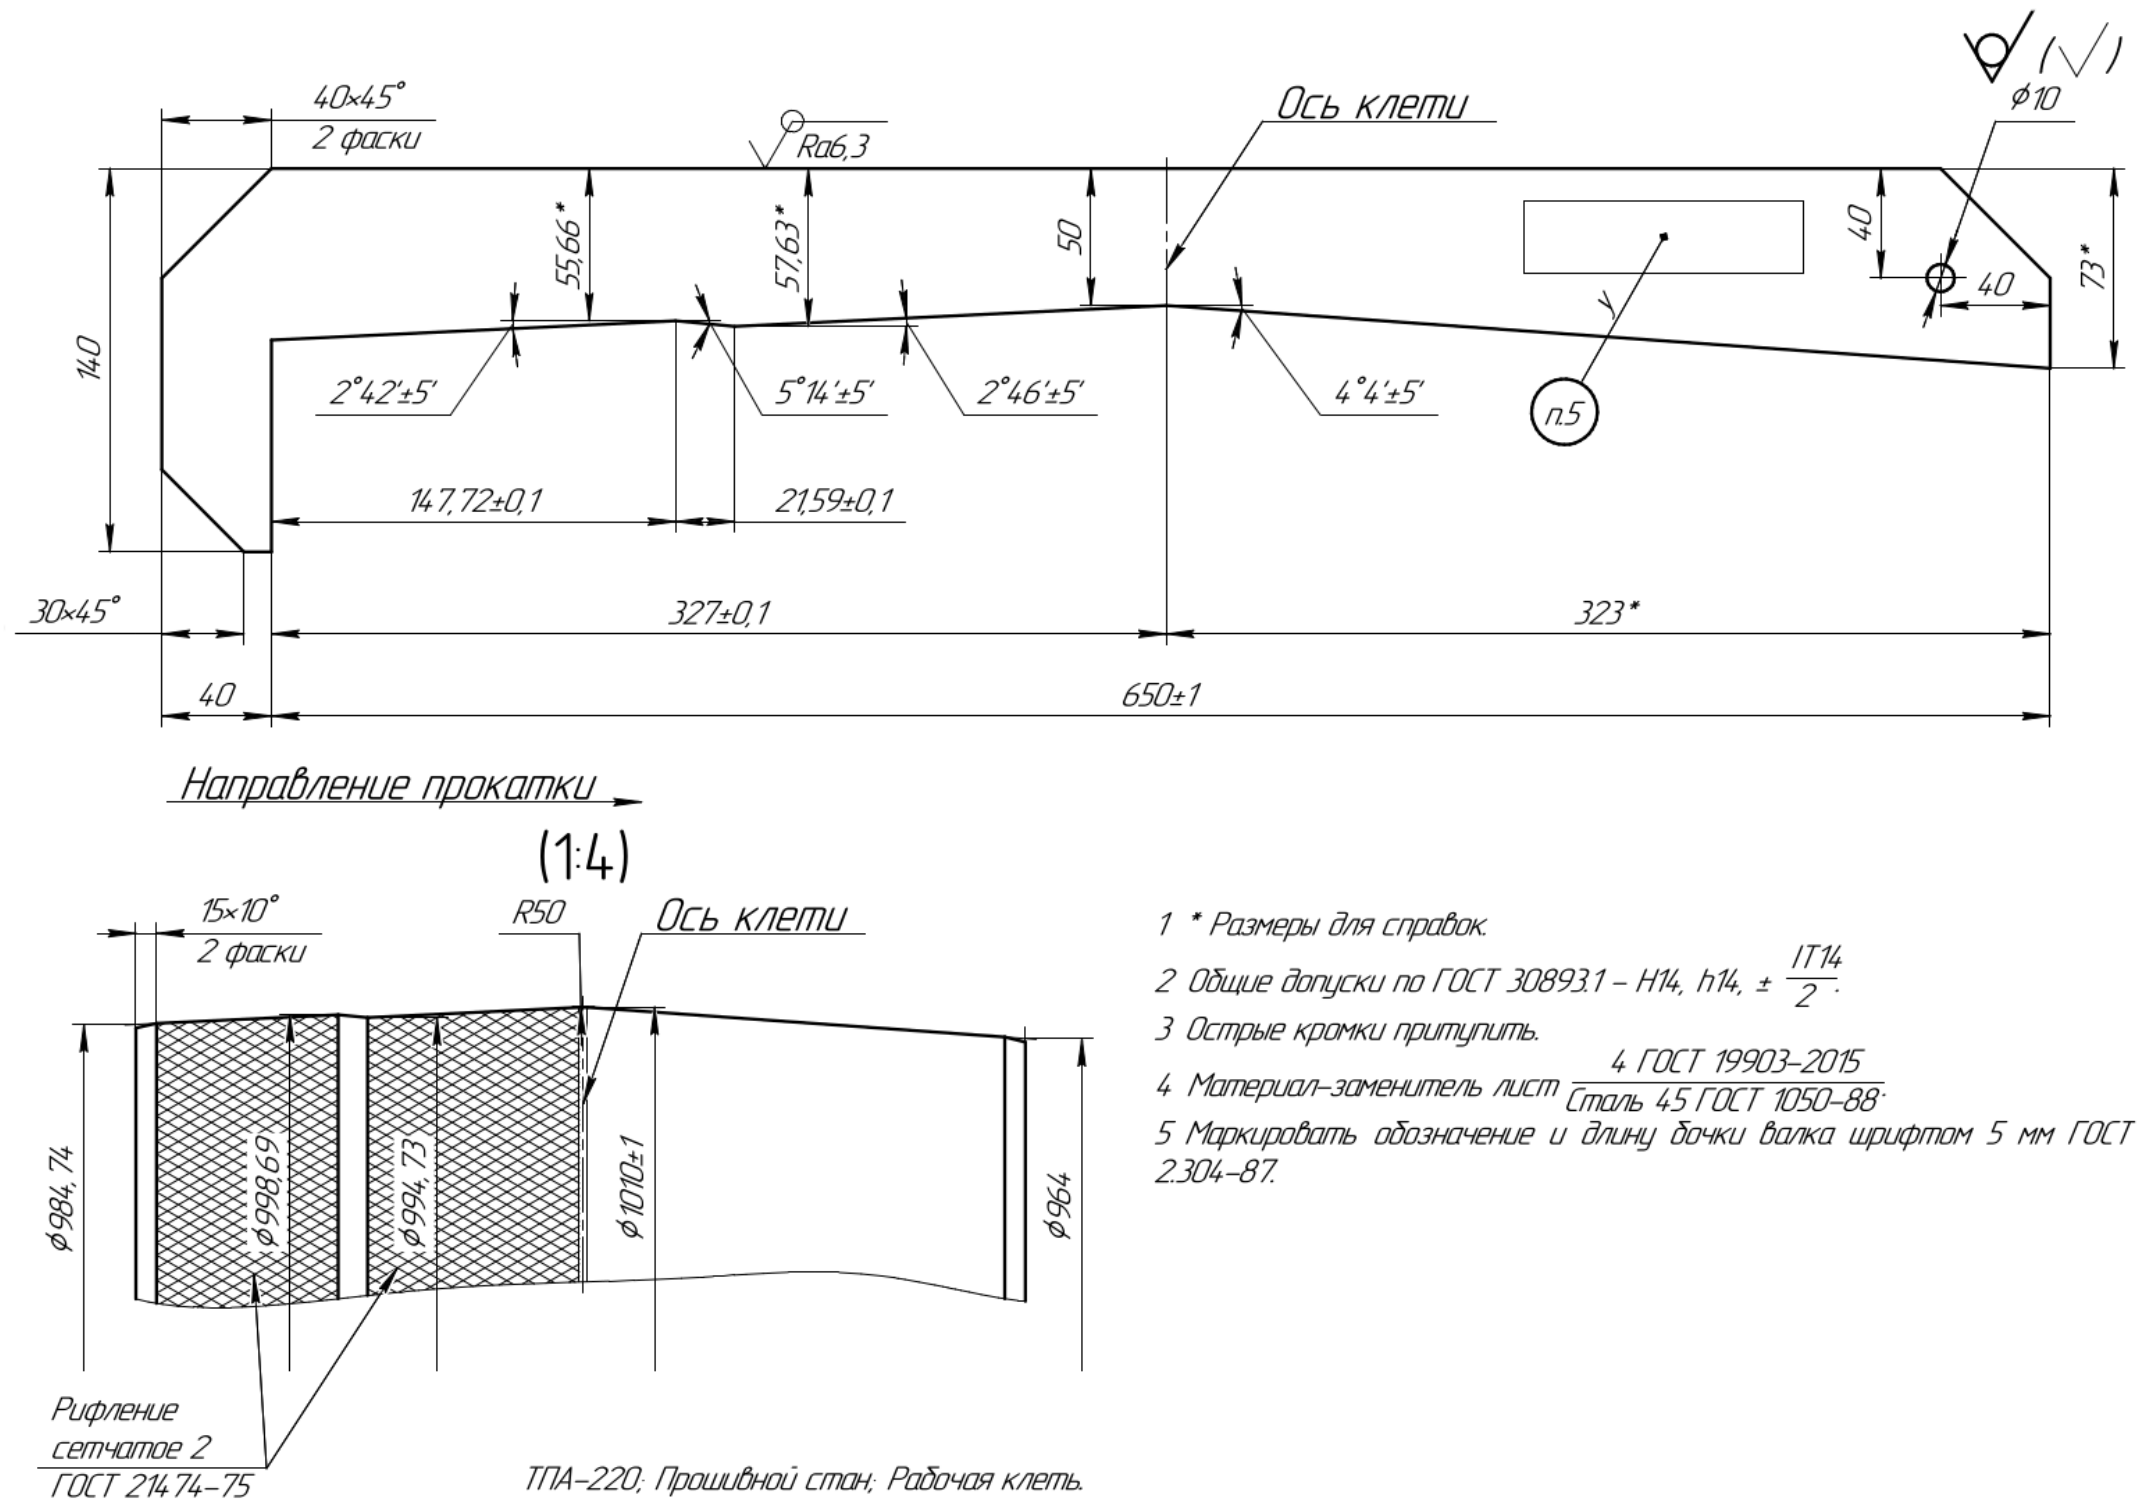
Чертеж калибровки рабочего вала ТПА 220
